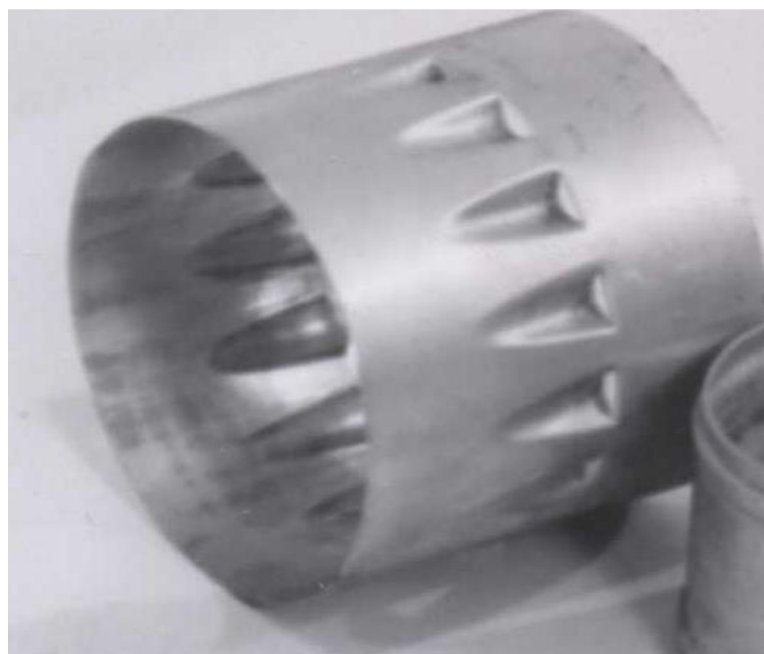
Общий вид трубы с прорубленными жалюзи
